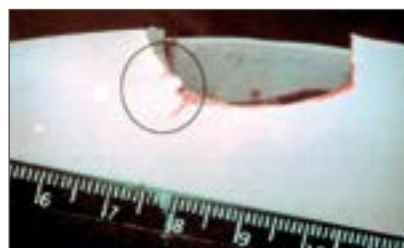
Внешний вид поврежденного диска из сплава VT20L
